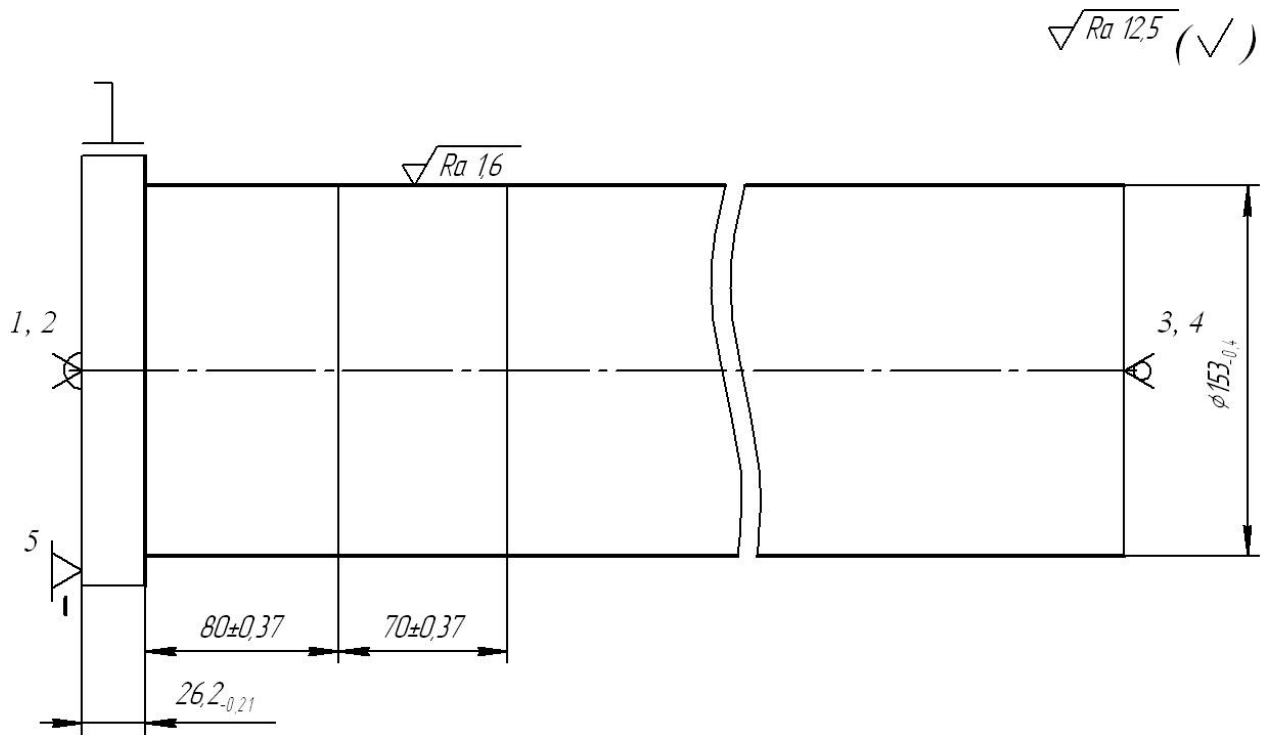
Схема базування заготовки на операції токарно-гвинторізній 020,
